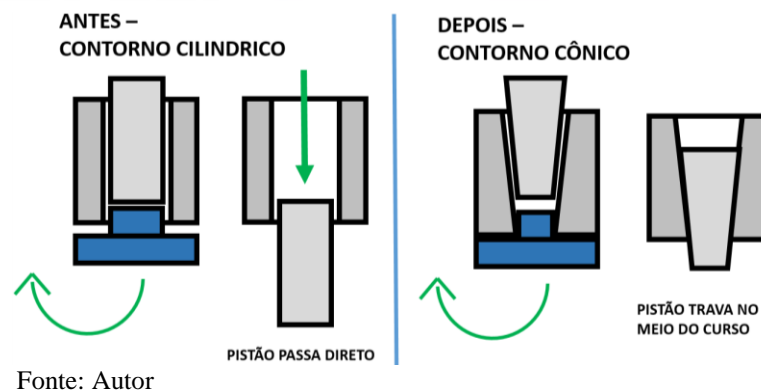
e 2 – Peças do molde e a sequência de encaixe do molde cilíndrico
